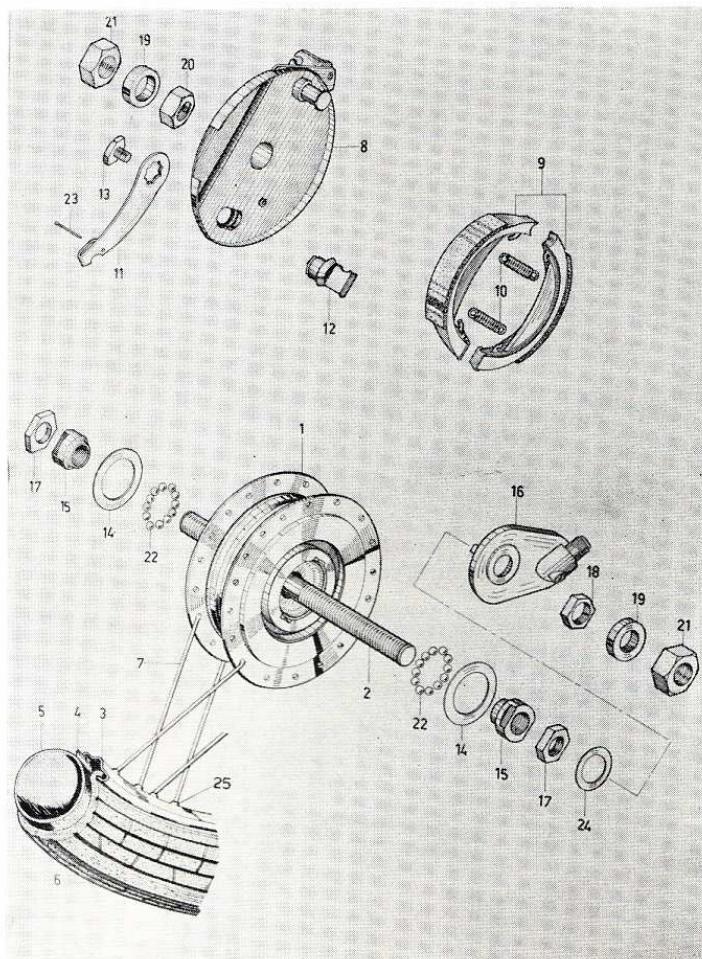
VUE ECLATEE DU MOYEU AVANT.
